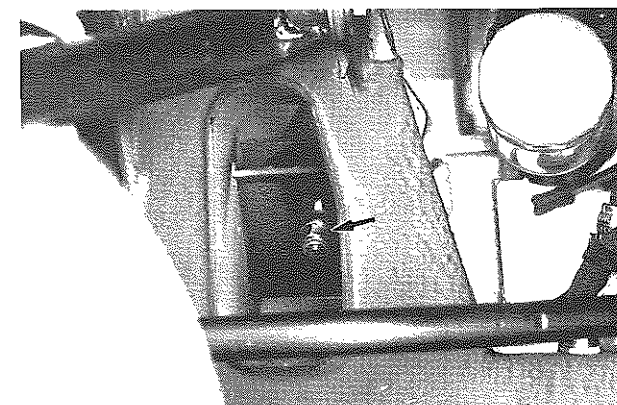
Viti di fissaggio laterale motore - Side engine screws
